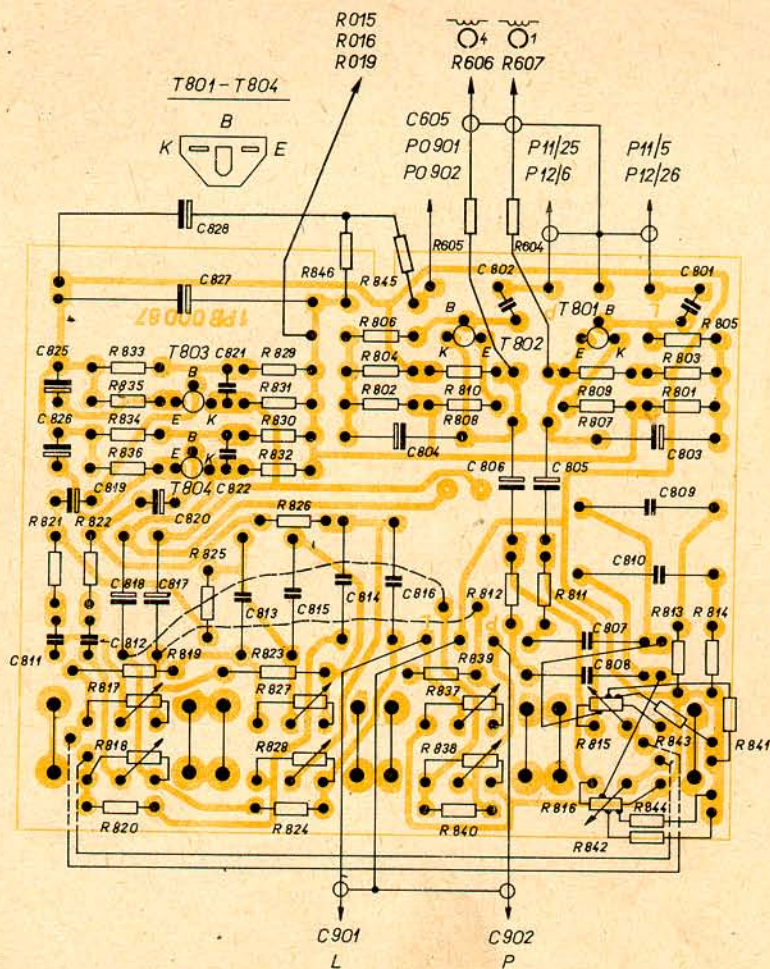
Montážní zapojení předzesilovače pro přenosku
